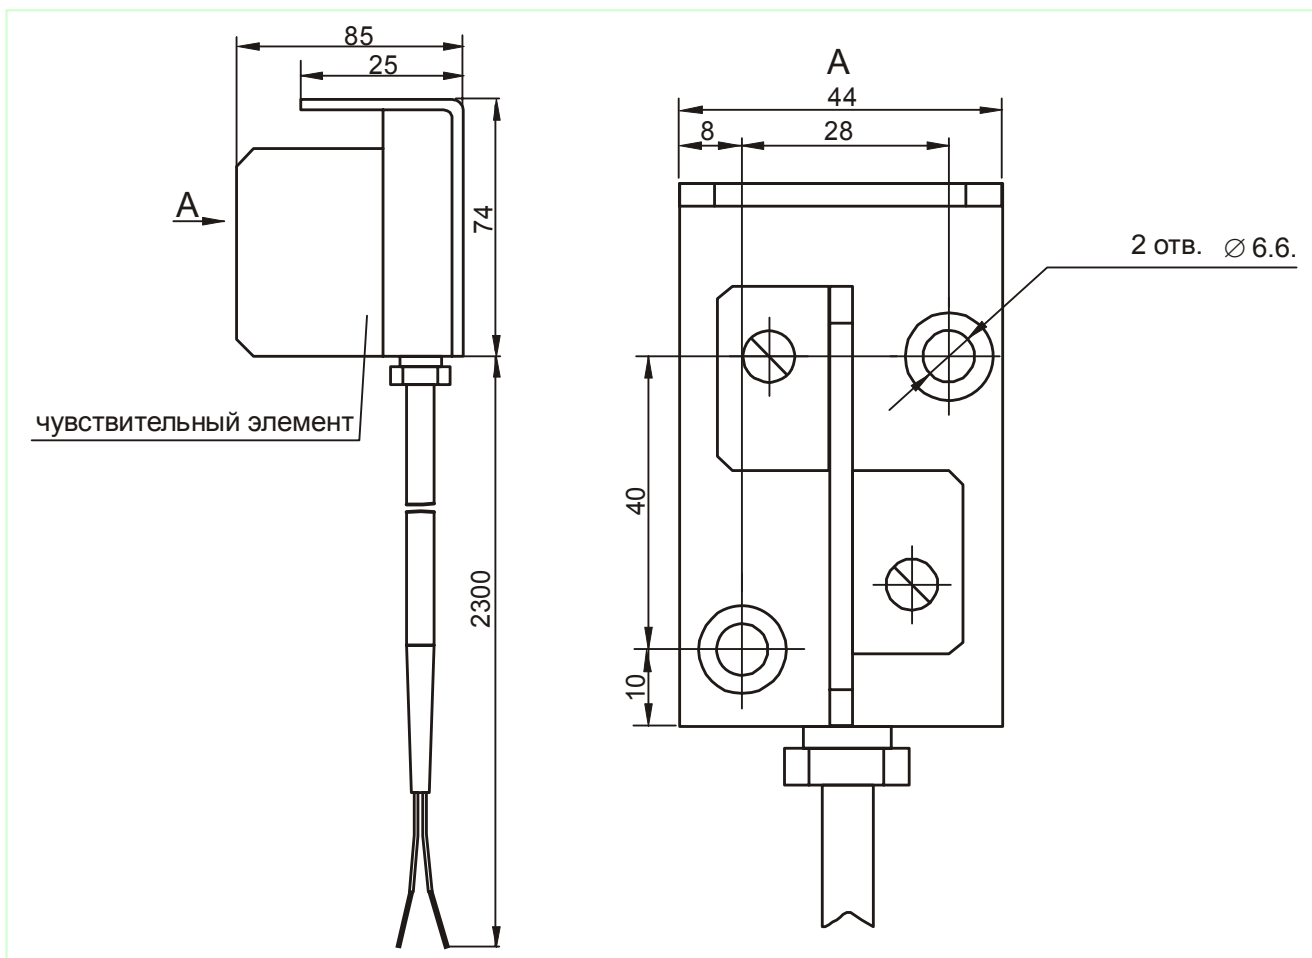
Внешний вид, габаритные и установочные размеры датчика С43
